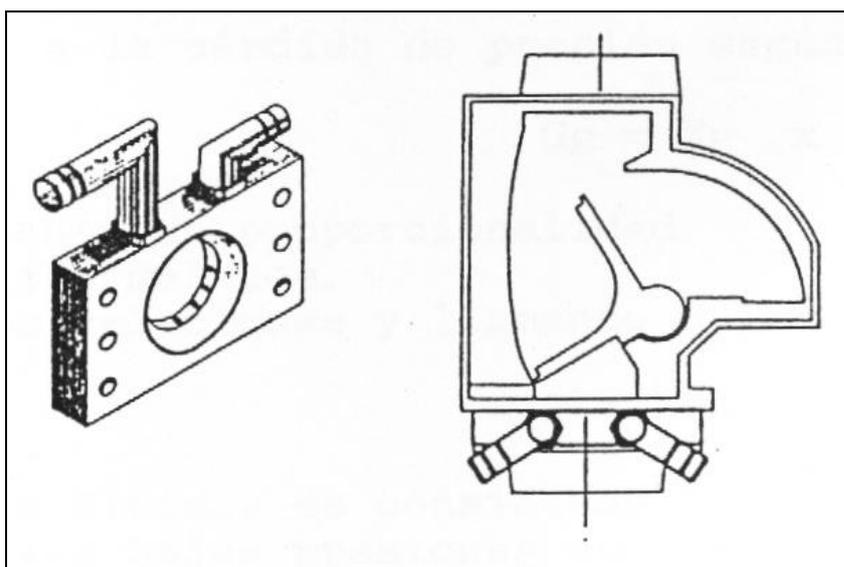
Montaje de un mezclador para sistemas de inyección L-Jetronic y Motronic
